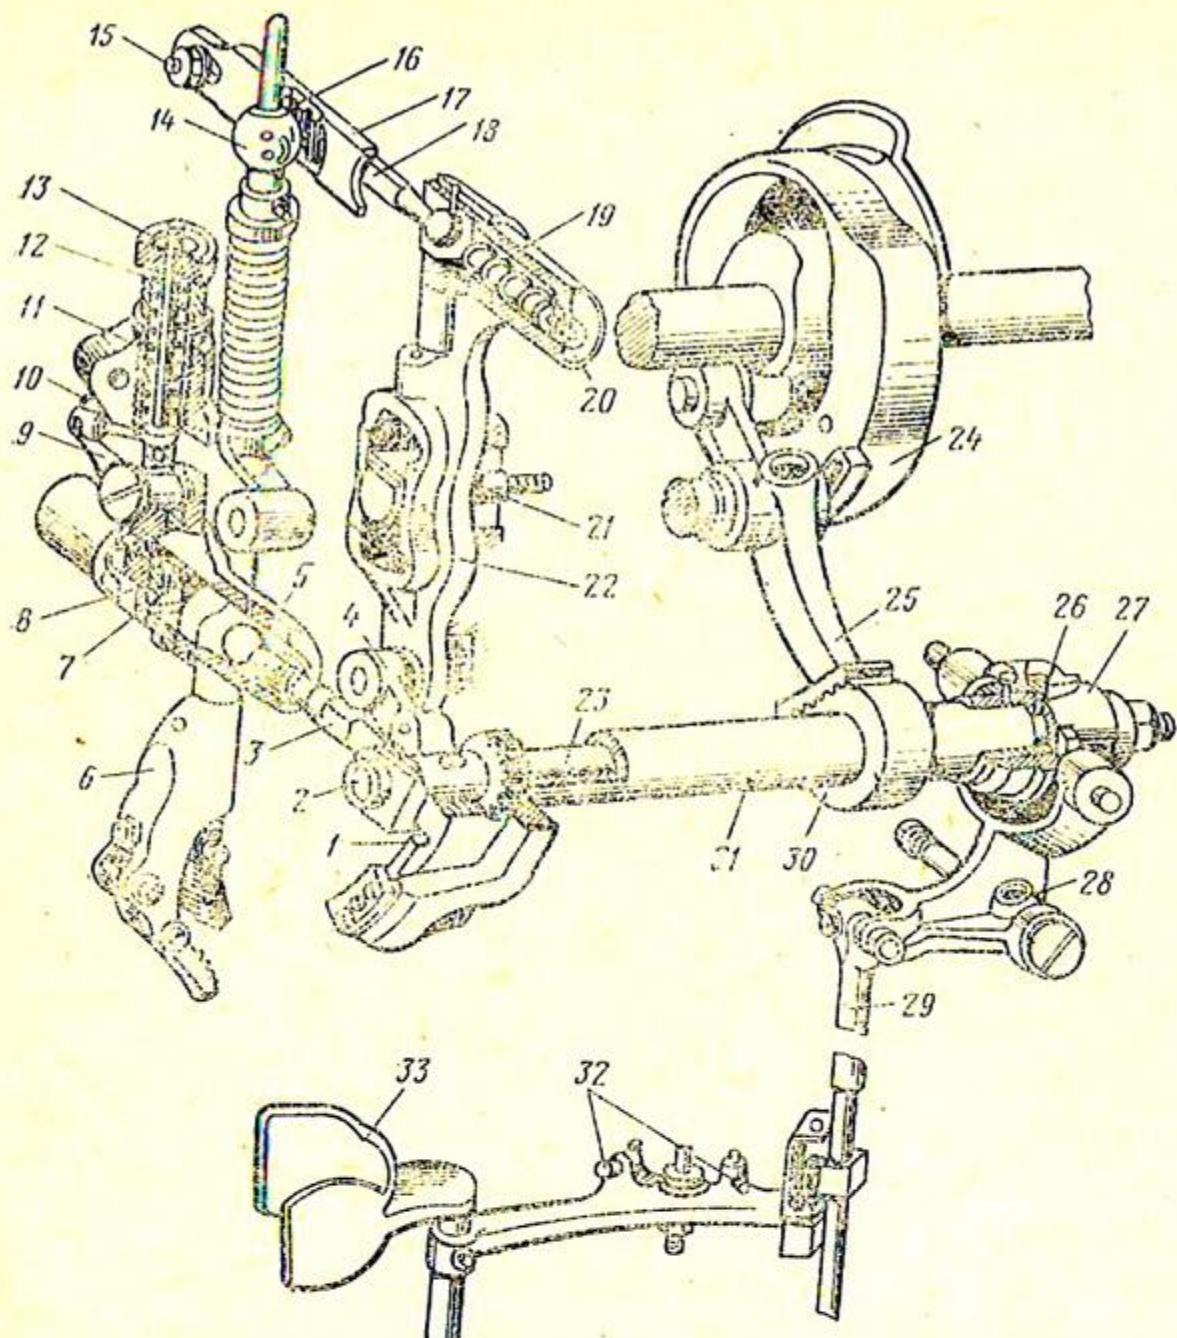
Механизм поворота и бокового перемещения клещей машины ЗВ-З-О
